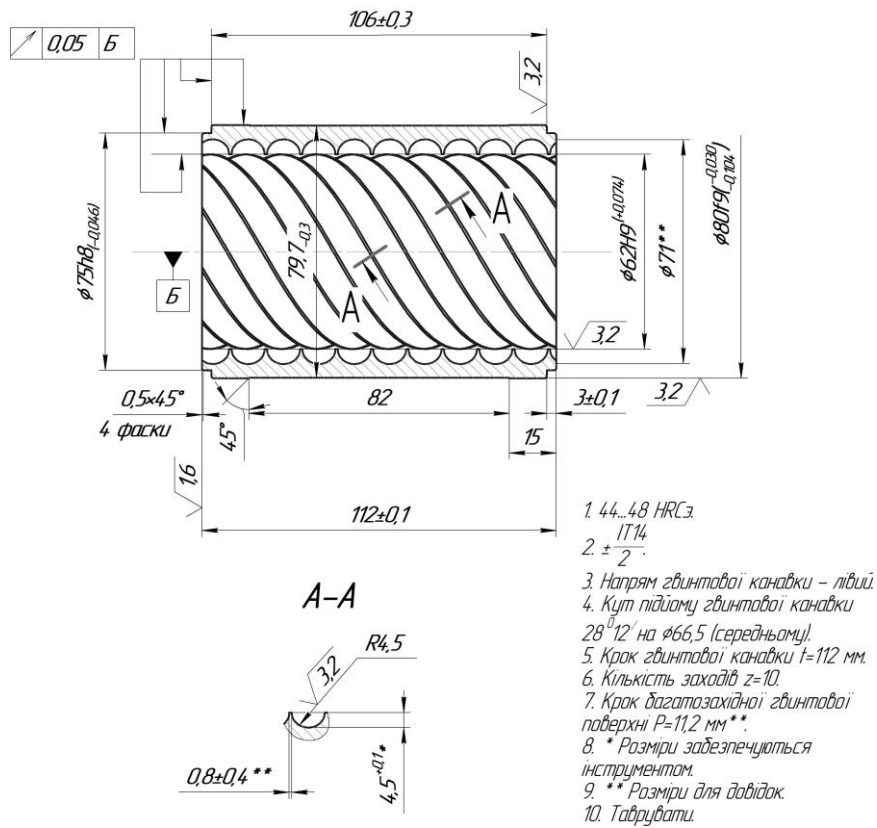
Креслення стандартної втулки ЛГН
